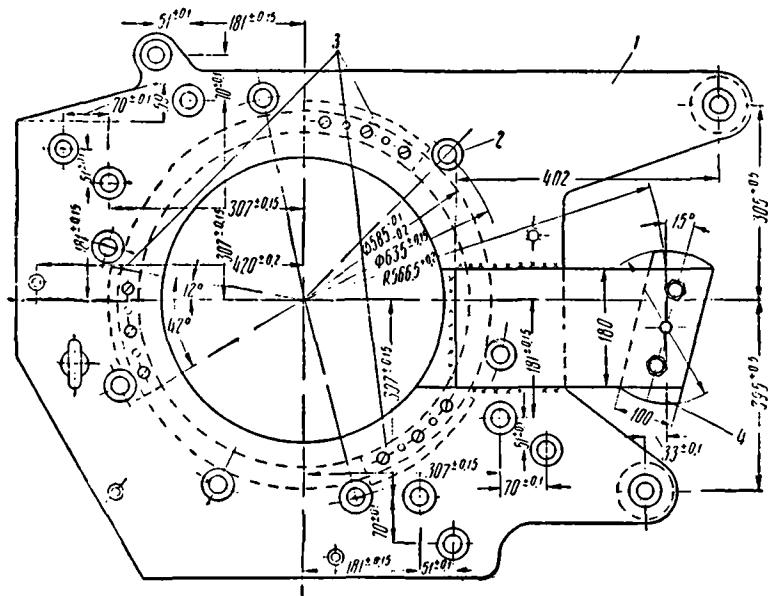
Кондуктор для сверления отверстий в осто́ве НБ-460 под подшипниковый щит со стороны коллектора:
